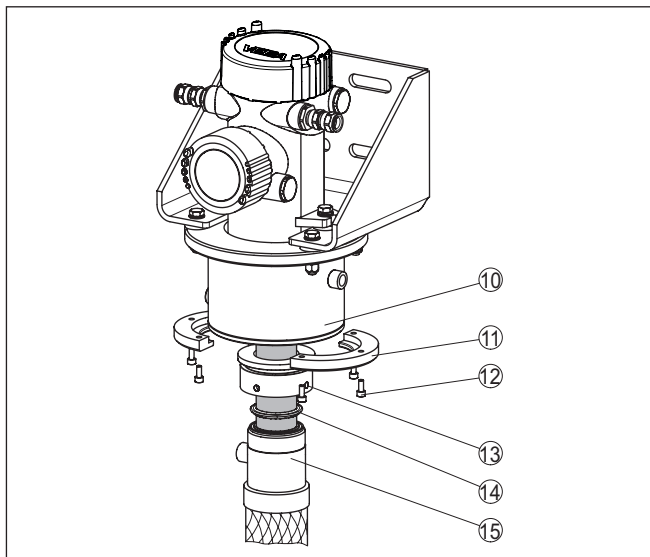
Montagem da refrigeração do cintilador - parte superior
